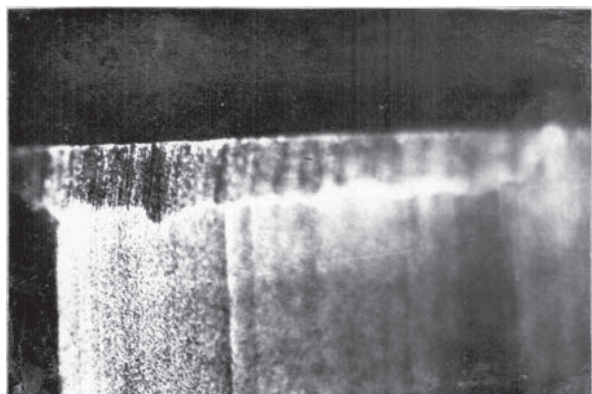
Вид износа резца из СВБН-5В при обработке покрытия из сплава ВК20КС
